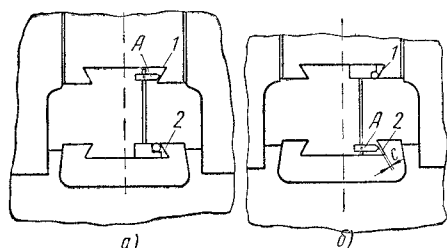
Приспособление для проверки параллельности привалочных плоскостей штамподержателя и бабы.
